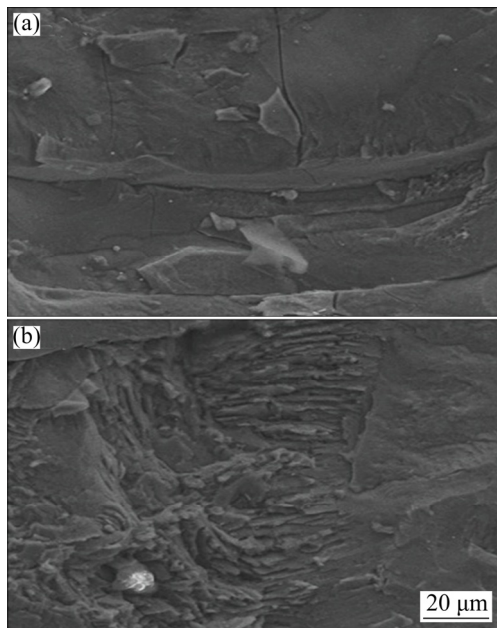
铝/钢激光焊接头剪切试样微观断口形貌
